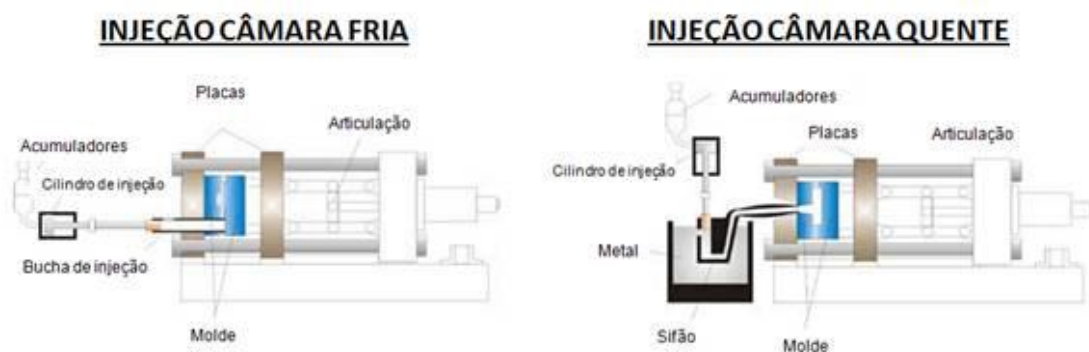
Esquemas de moldagem sob pressão (Fonte: www.ebah.com.br)
